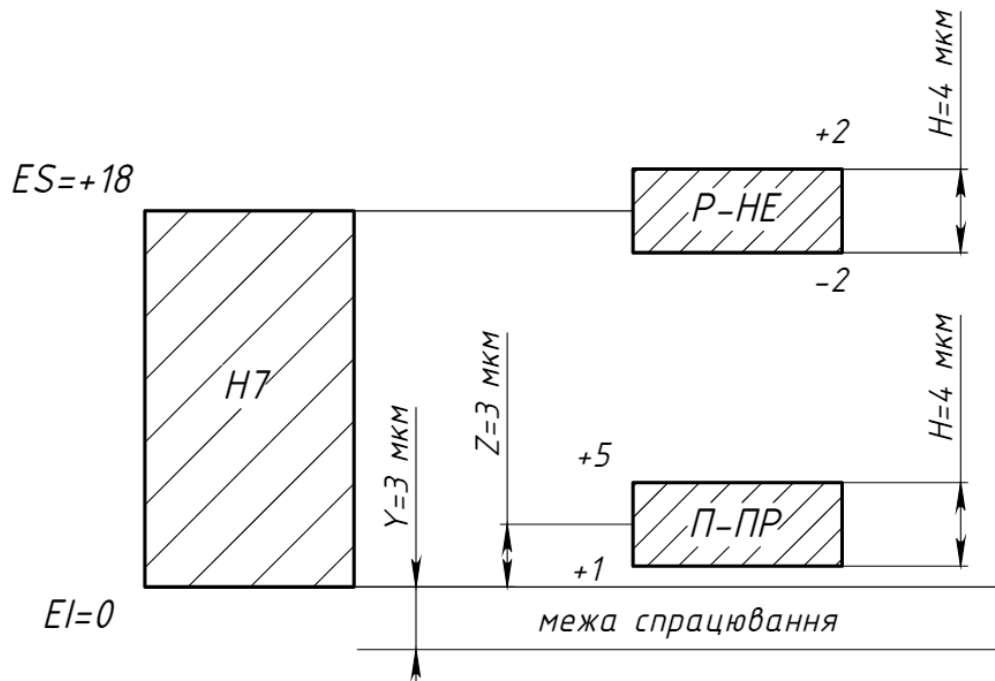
Схема розташування поля допуску для калібр-пробки
